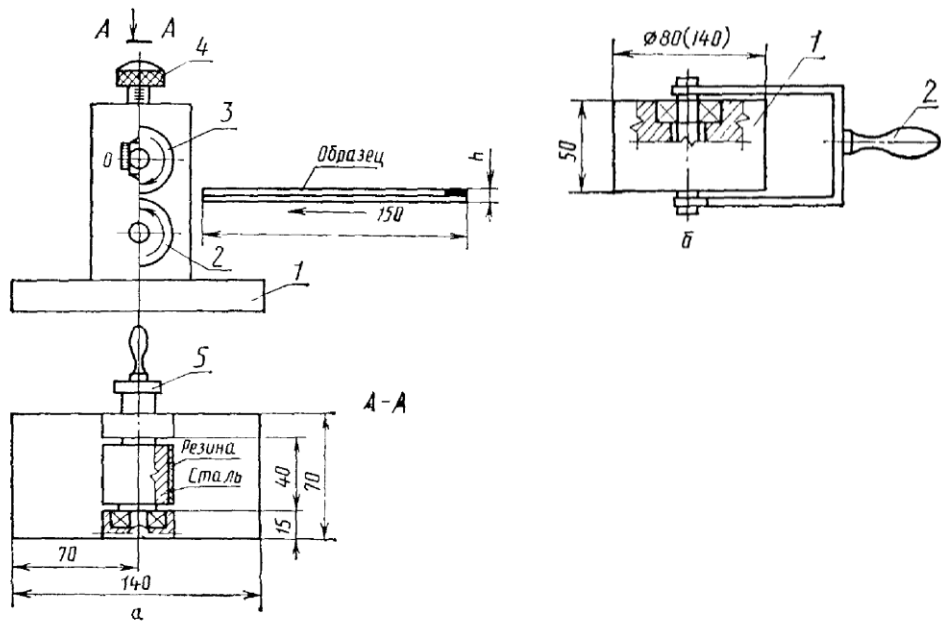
Устаткування для формування клейового шва: *a* – механічний пристрій: 1 – основа; 2 – відомий валик діаметром 40 мм; 3 – ведучий валик діаметром 40 мм; 4 – регулювальний гвинт; 5 – рукоятка (привід);
